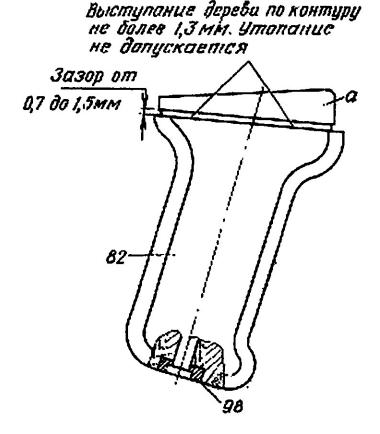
Подгонка рукоятки: а — наконечник рукоятки: 82 — рукоятка; 98 втулка соединительного випта
